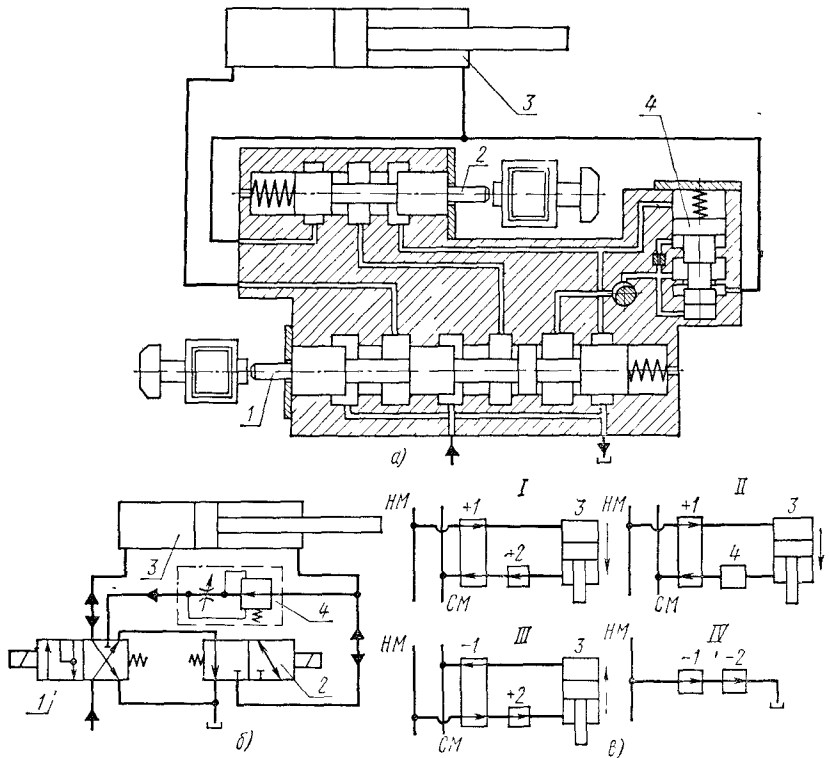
Полуконструктивная (а), полная (б) и попереходная (в) схемы силовой головки агрегатного станка
